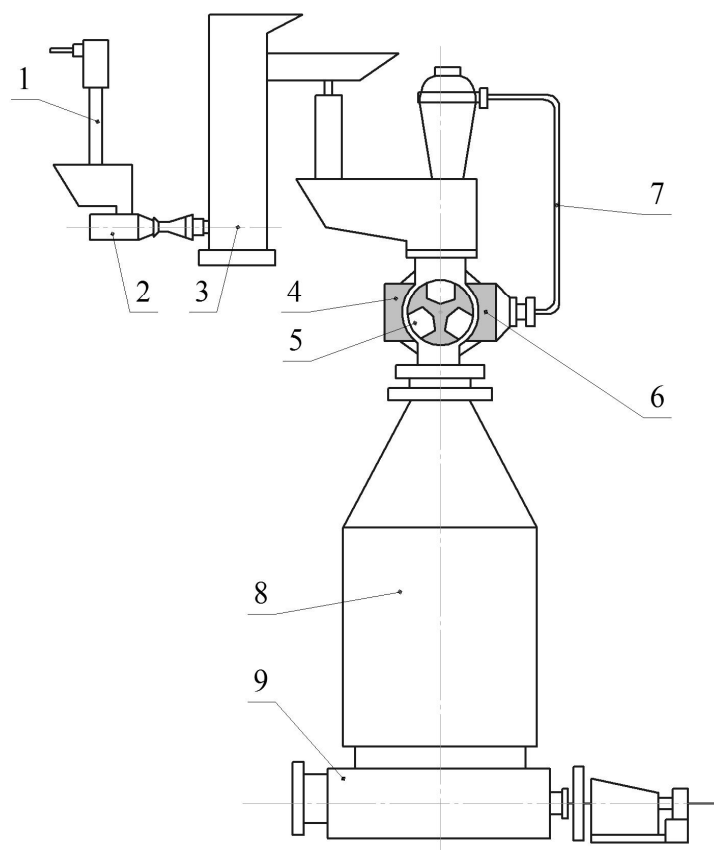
Схема работы установки ПТ непрерывной варки типа «Бауэр»
